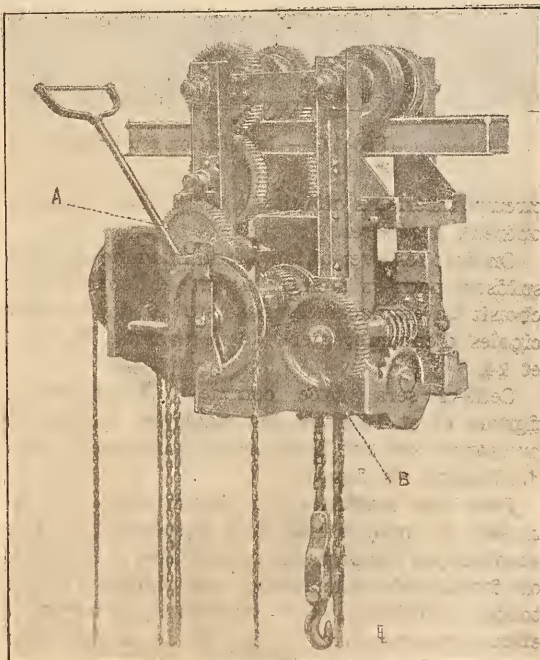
Exemple de commande par vis sans fin : A, moteur ; B, engrenage.
